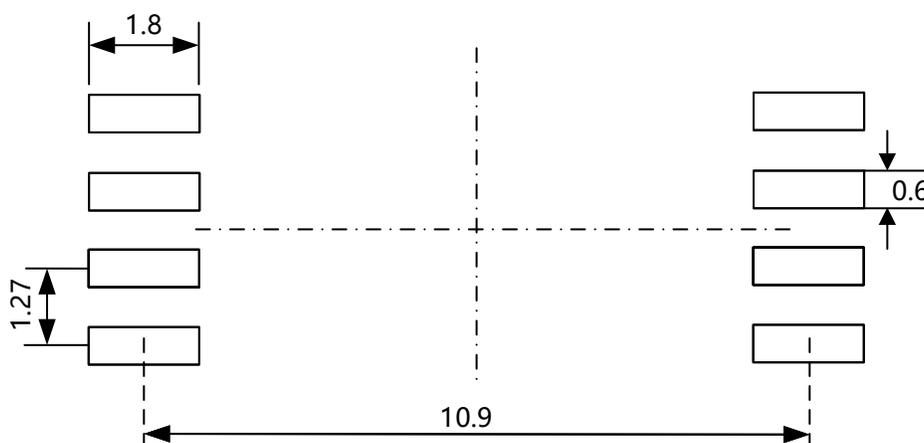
PCB 焊盘: 8-引脚 SOW
